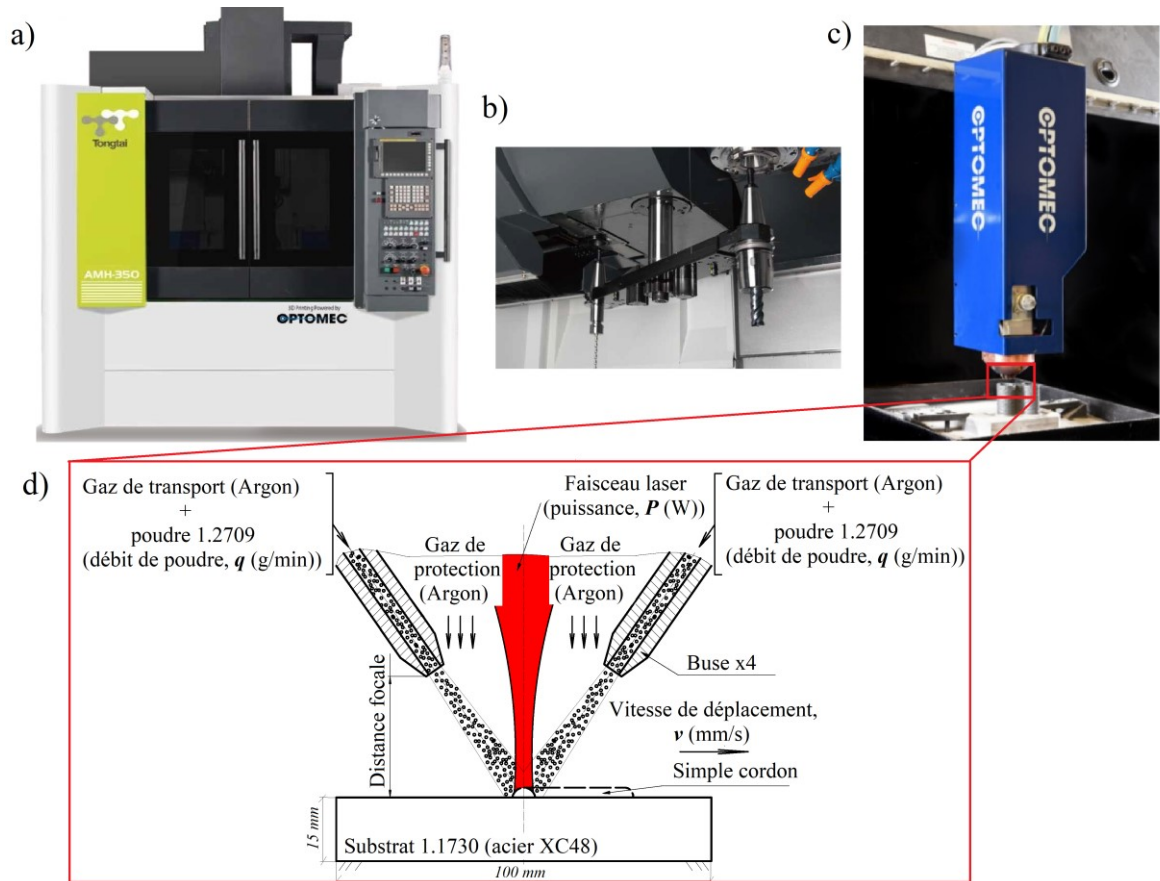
Vue générale de la machine LMD hybride AMH-350 (a), partie centre d’usinage (b), partie tête laser « multi-jet » (c), schéma et paramètres de rechargement (d)
